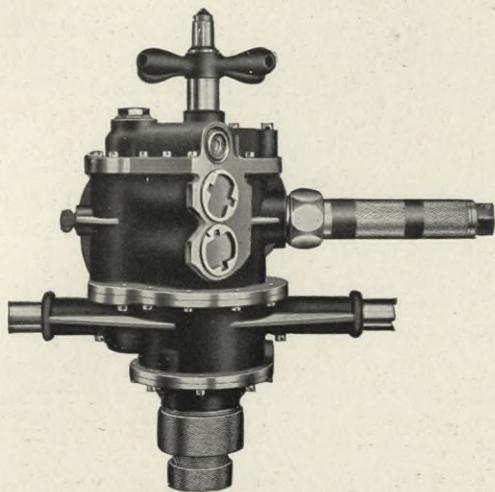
Preßluftbohrmaschine mit Compoundvorgelege zum Gewindeschneiden (schwerere Bauart)
